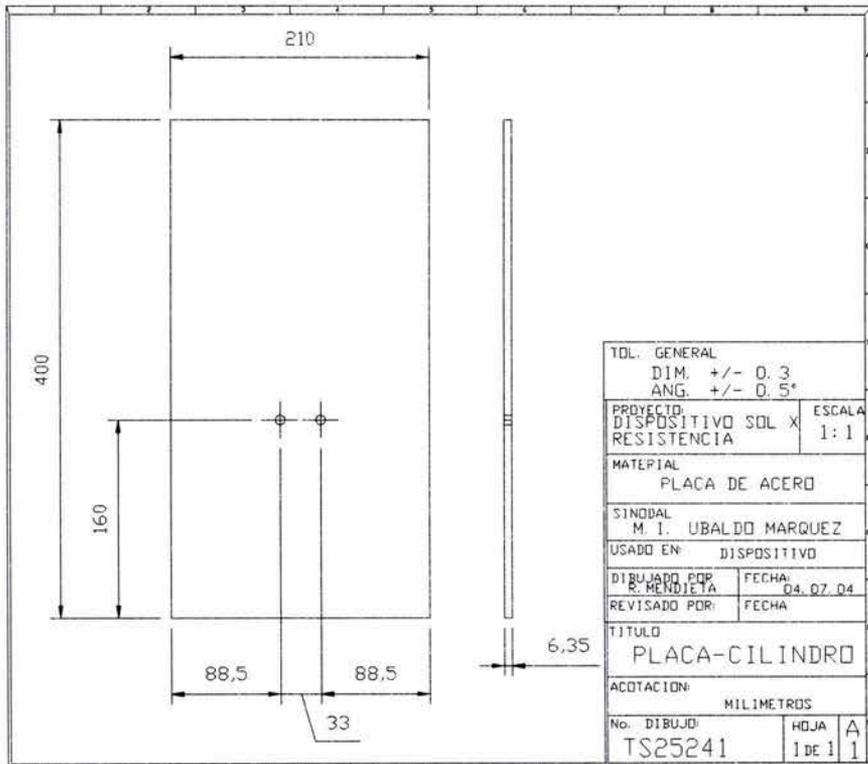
Placa para sujetar el cilindro en la estructura de la herramienta.
